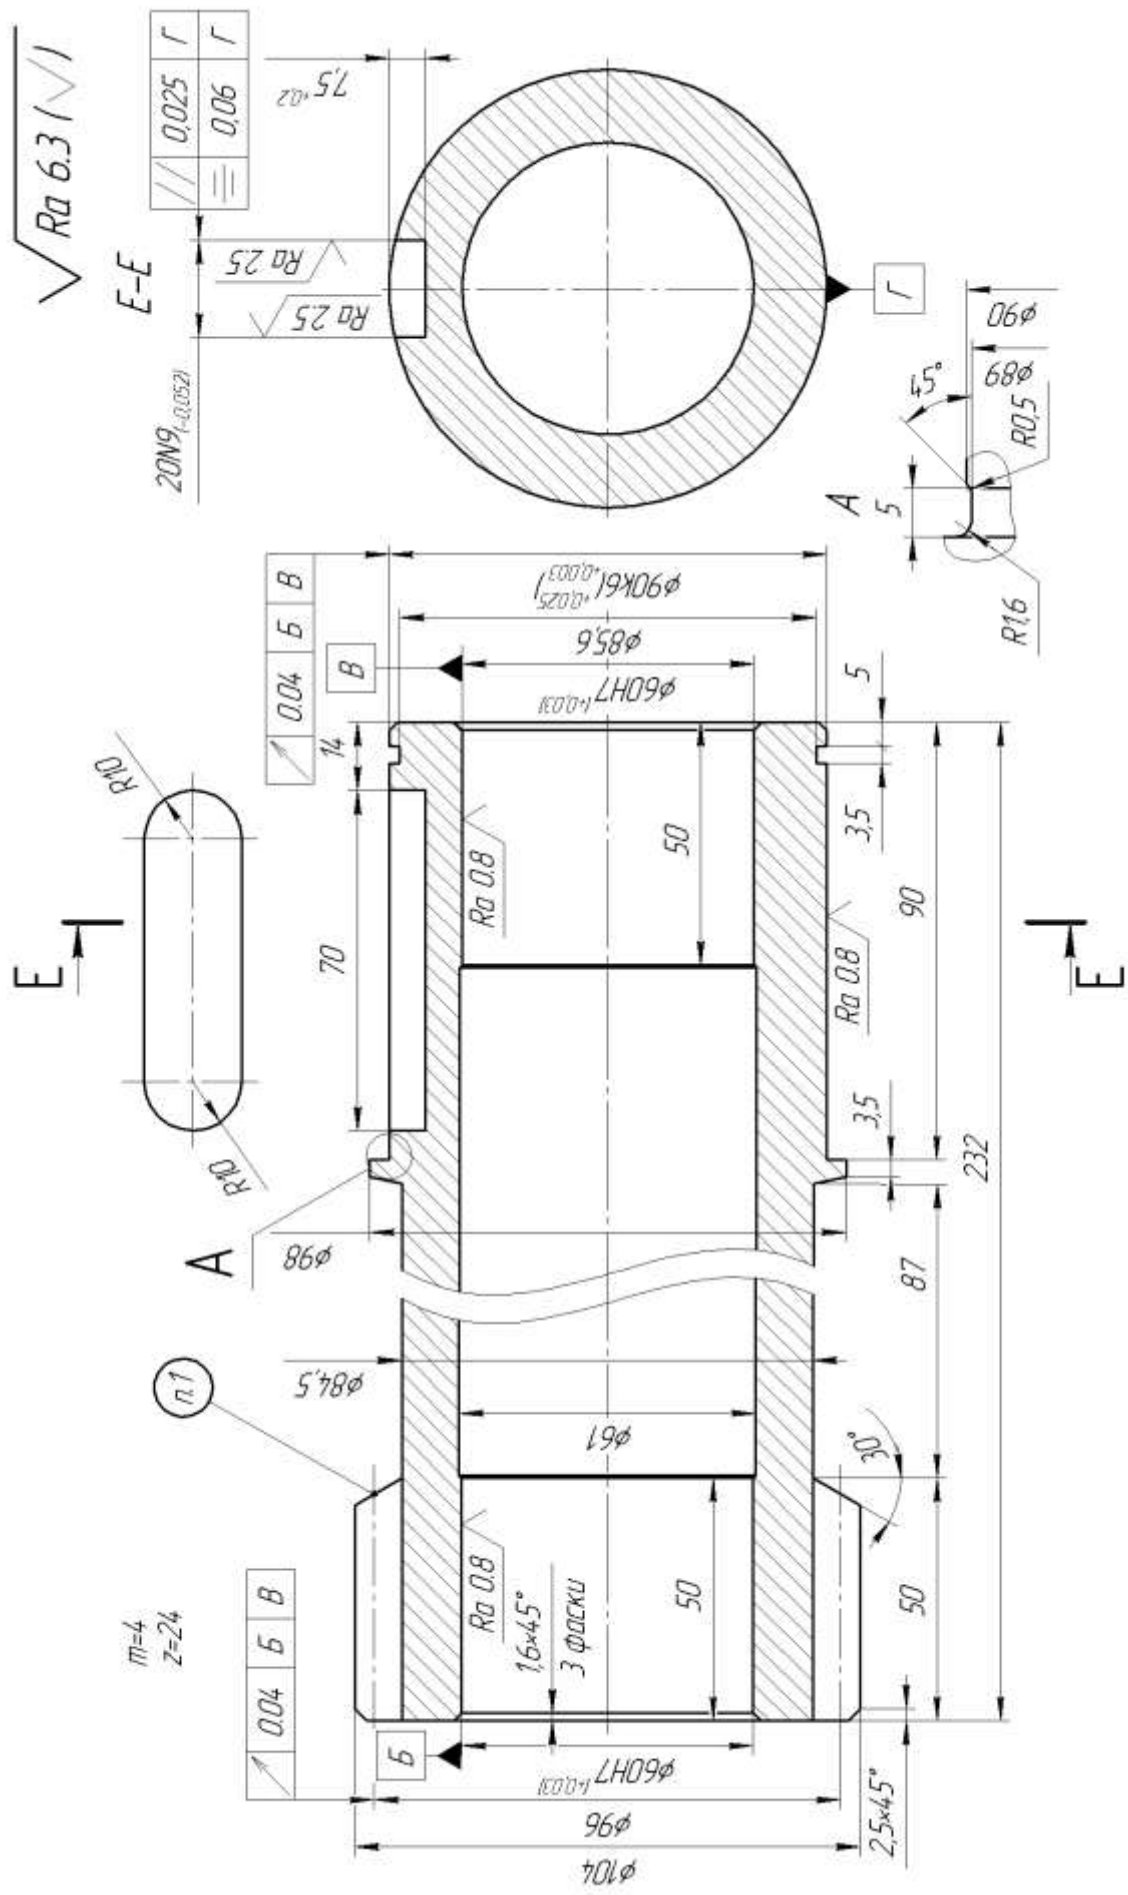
Креслення деталі «Проміжний вал»
